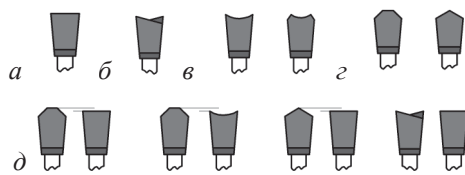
Формы зубьев дисковых твердосплавных пил:
